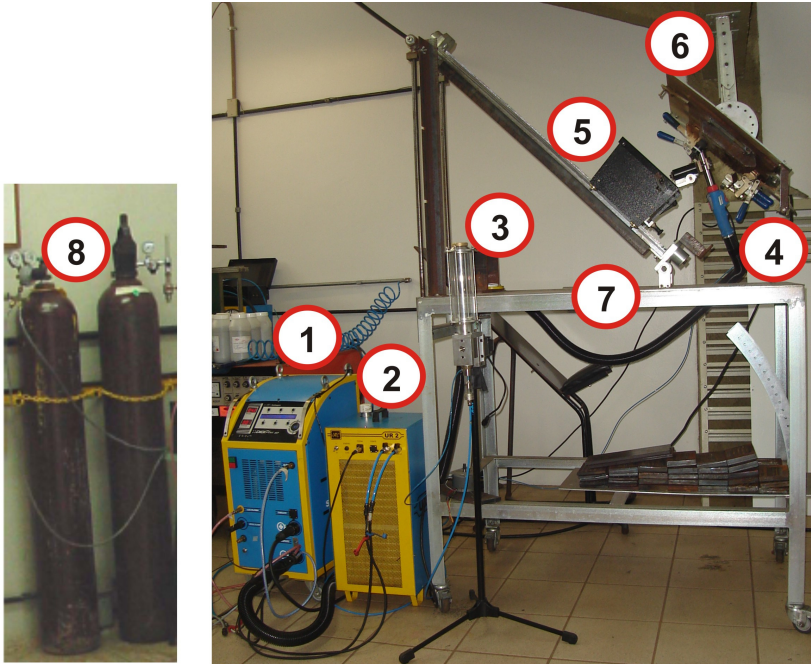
Bancada de soldagem PTA-P (LABSOLDA)
